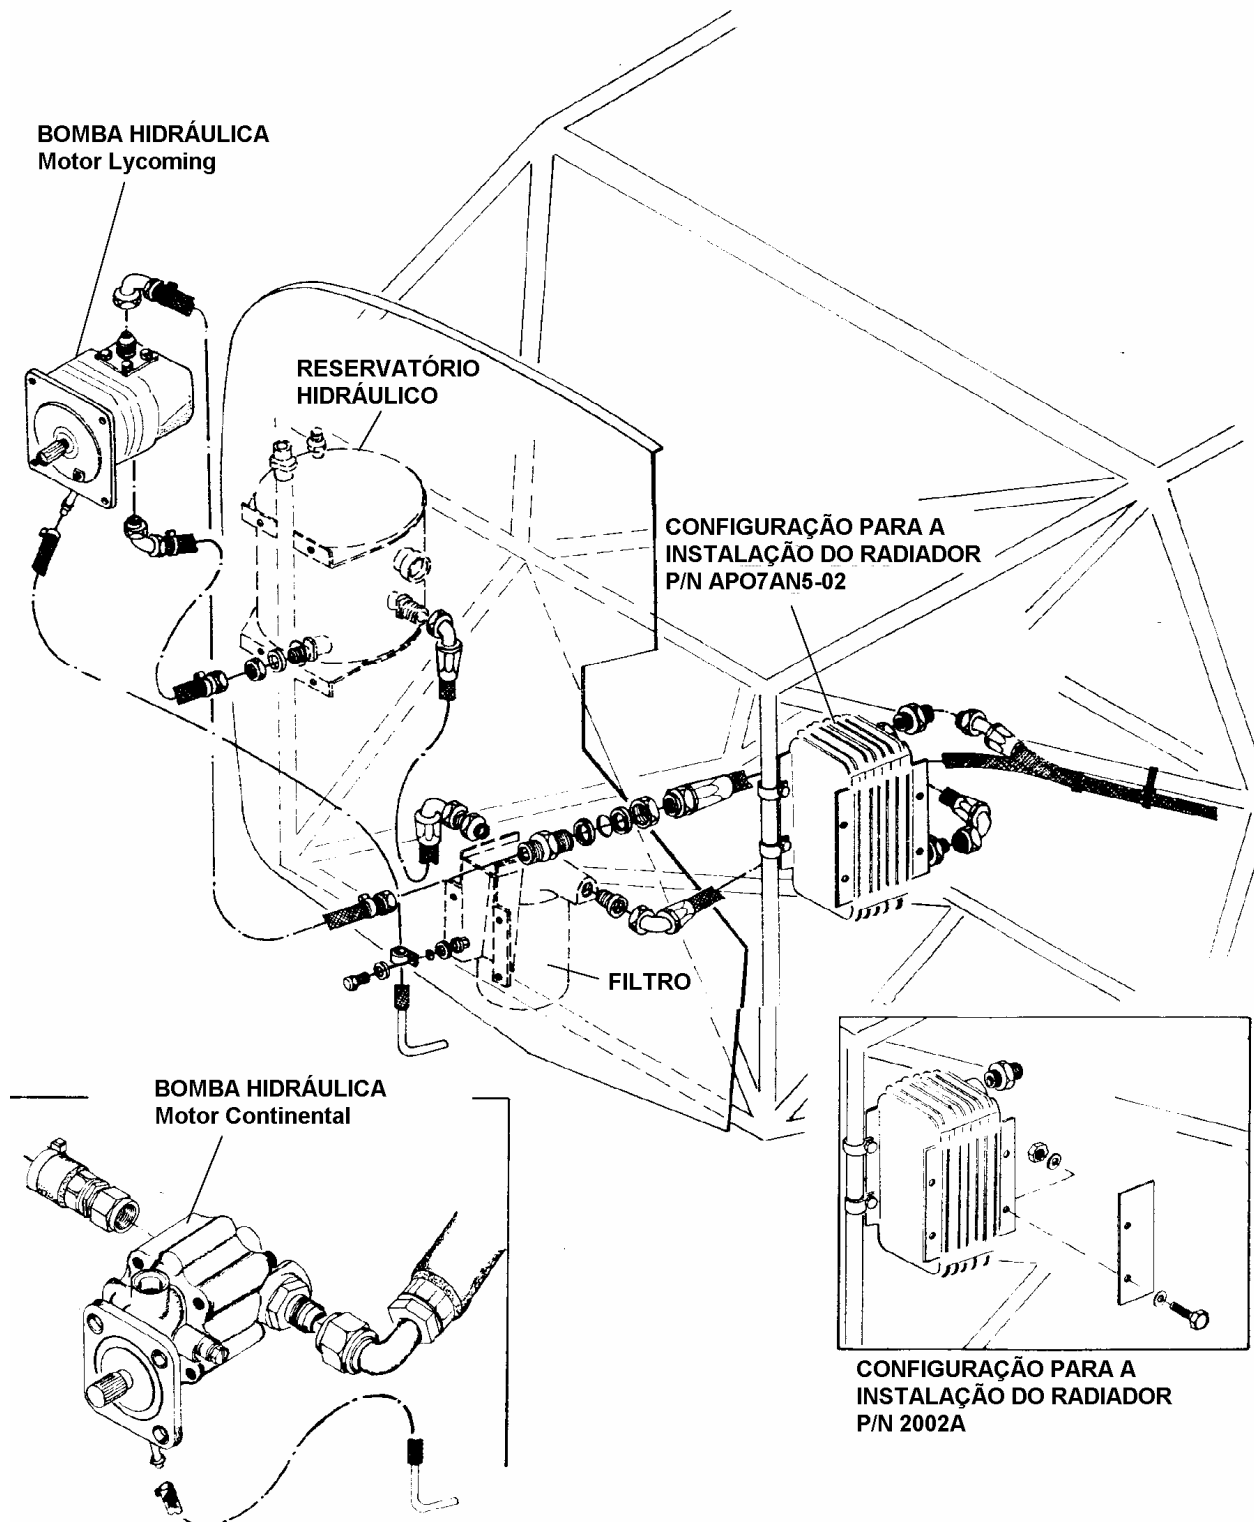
Instalação do Sistema de Pulverização (Folha 1 de 5)
